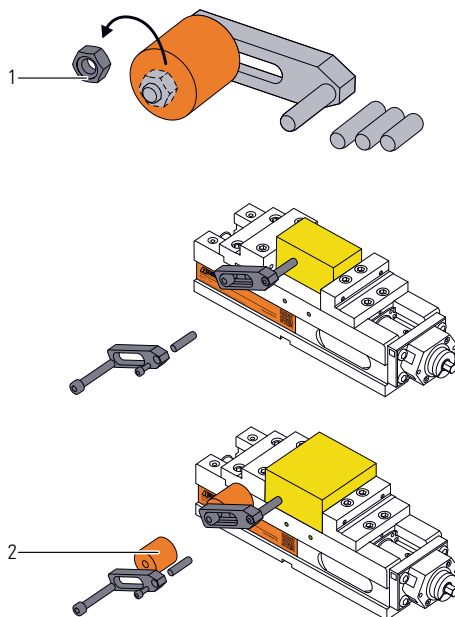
Упор обрабатываемой детали 692 168 5670 042
